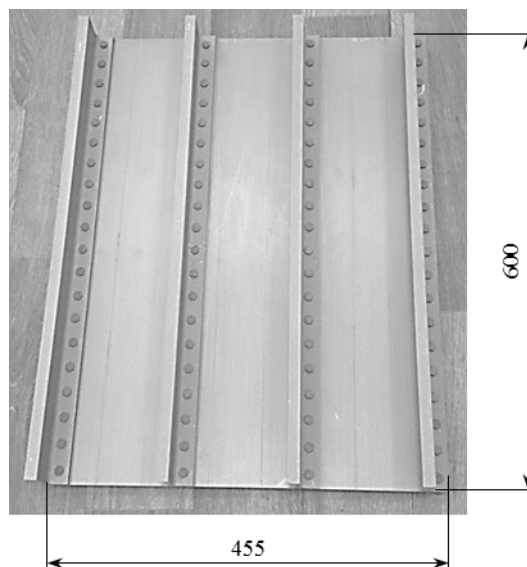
Конструктивно-подобный образец из прототипа гибридной панели крыла для испытаний на сжатие
